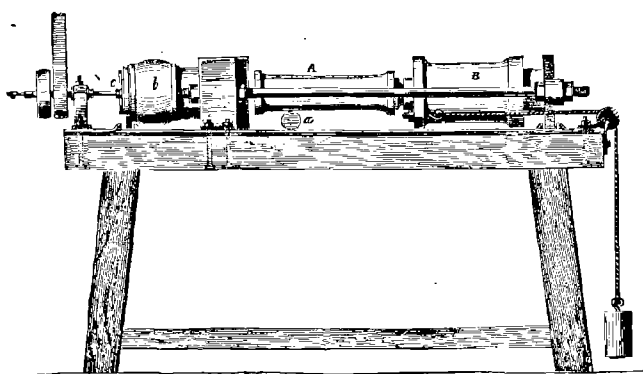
Machine à fabriquer les pâtes d'Italie.
